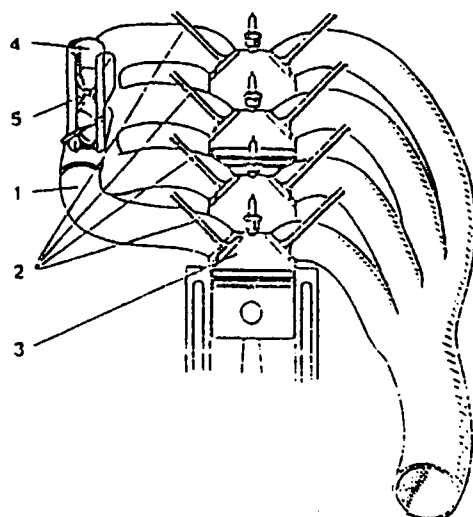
Esquema que muestra la disposición clásica del montaje de un Carburador en el motor.
